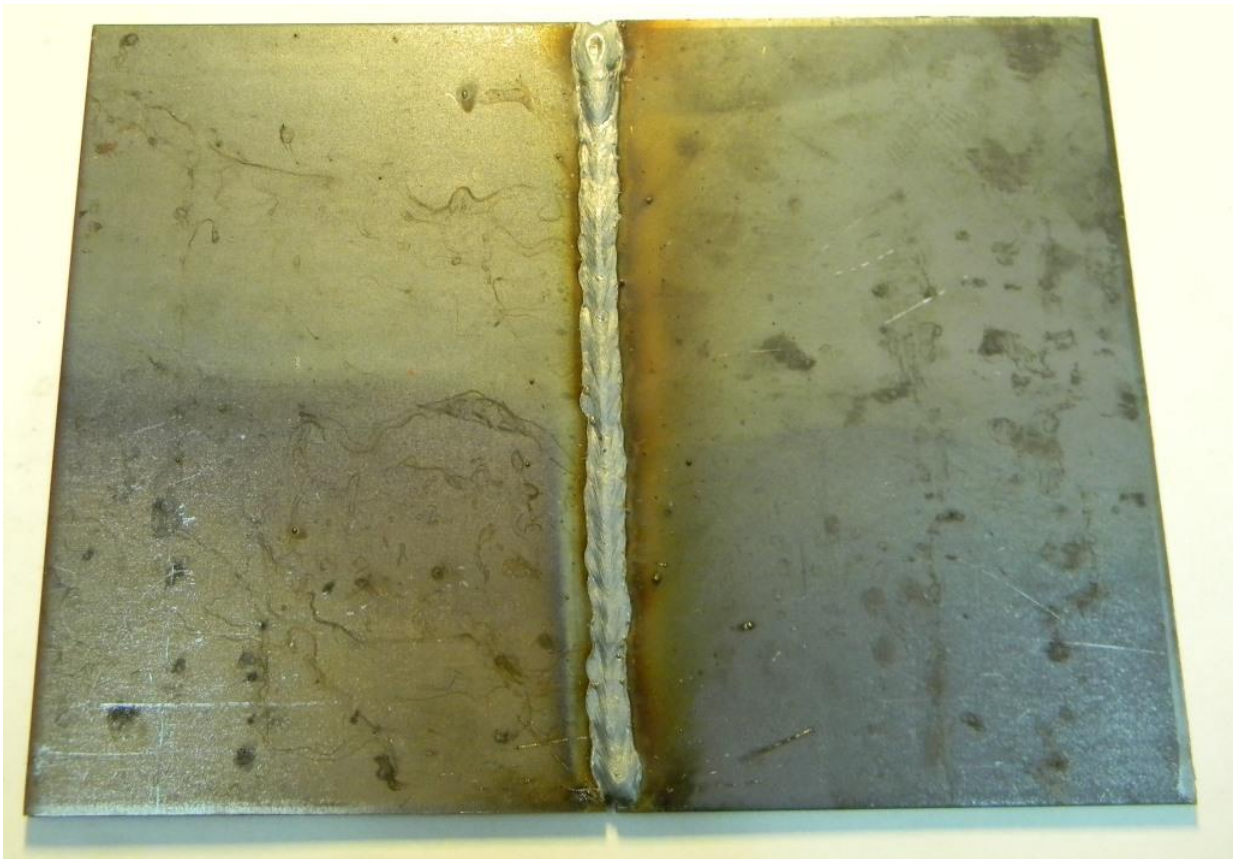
Образец после сварки подготовленный вырубкой контрольная без очистки вид сверху
